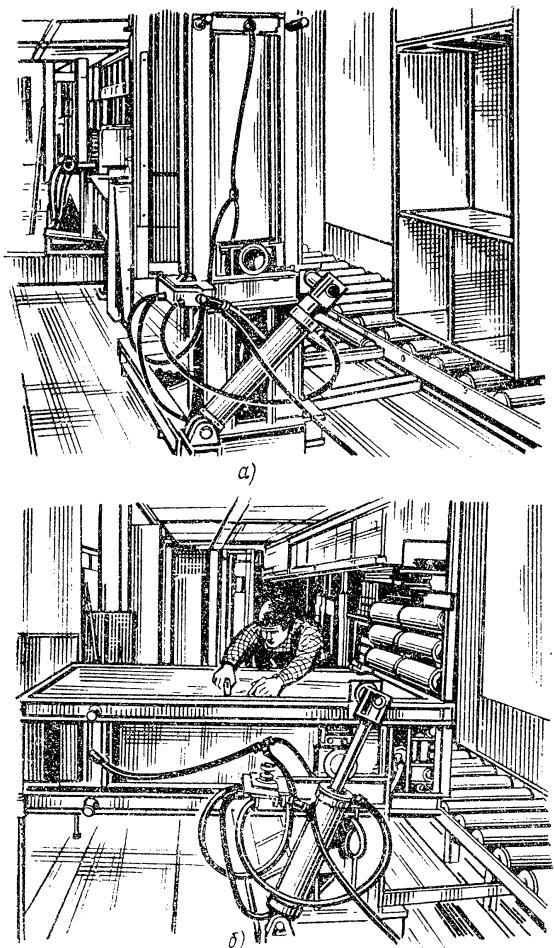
Стапельная сборка корпуса (а) и установка задней стенки (б)
